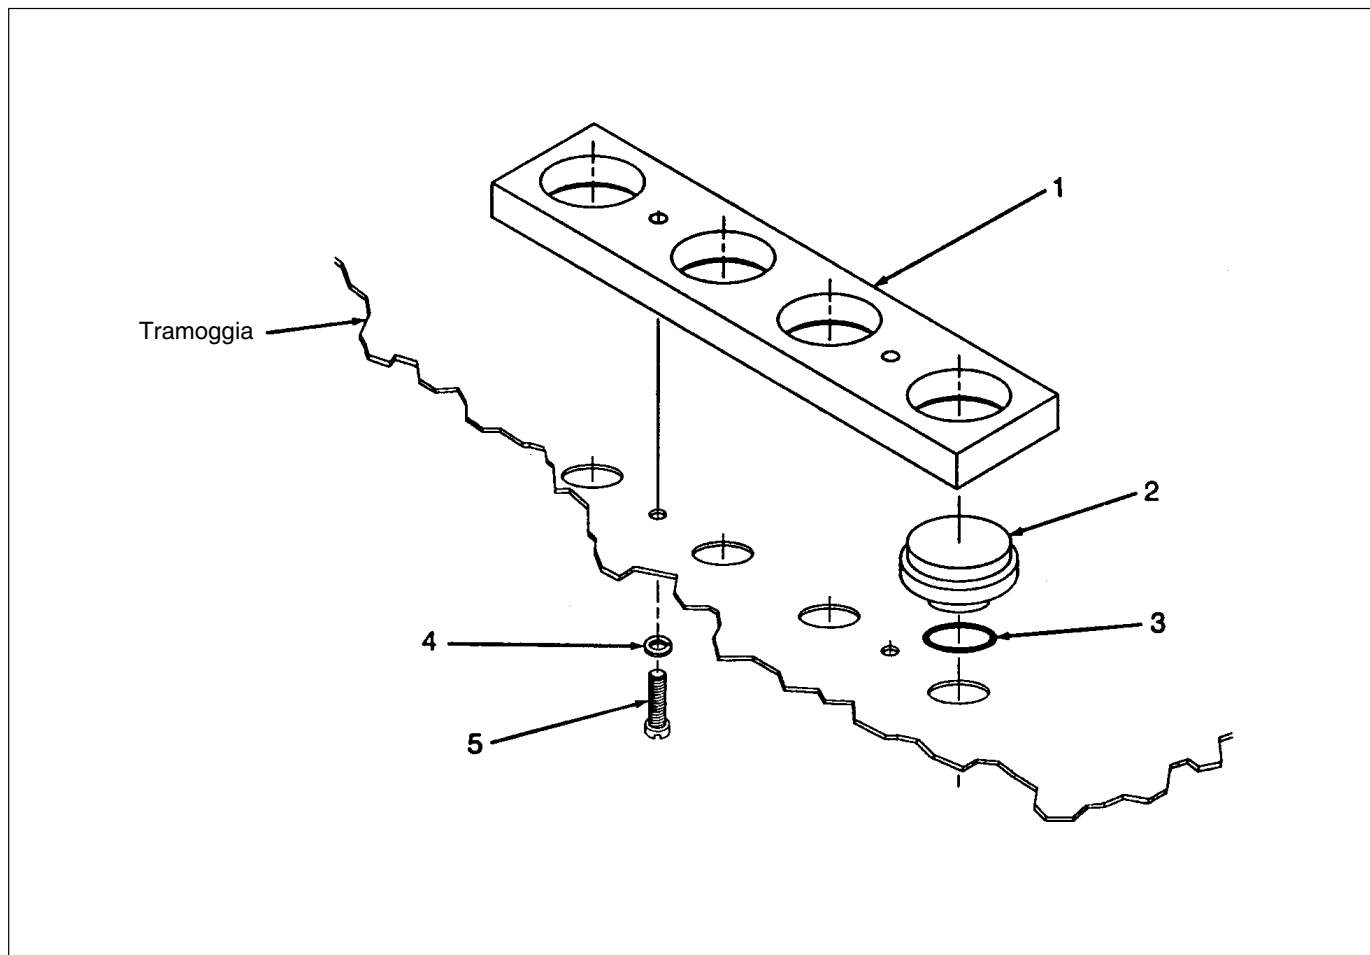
Disegno esploso kit di montaggio pompa multipla
